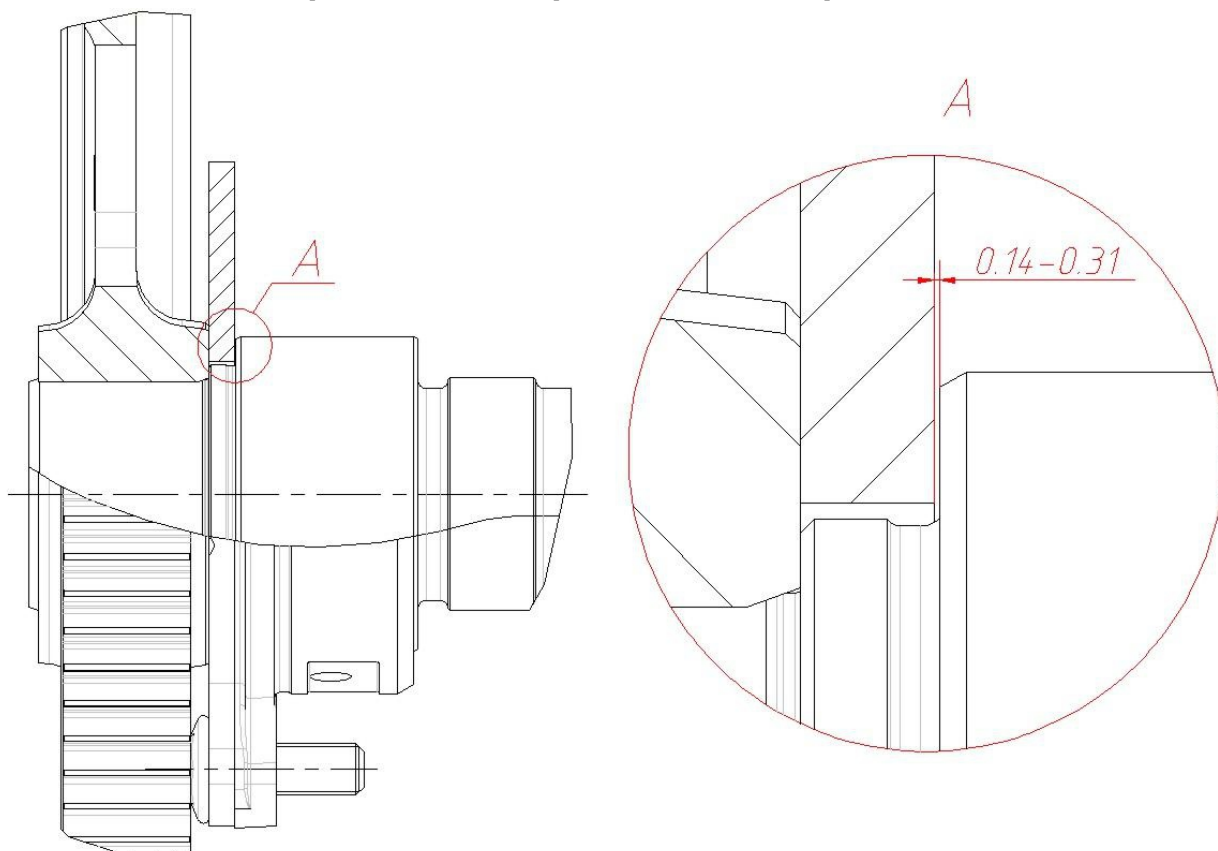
Зазор: упорный фланец - торцевая поверхность опорной шейки
